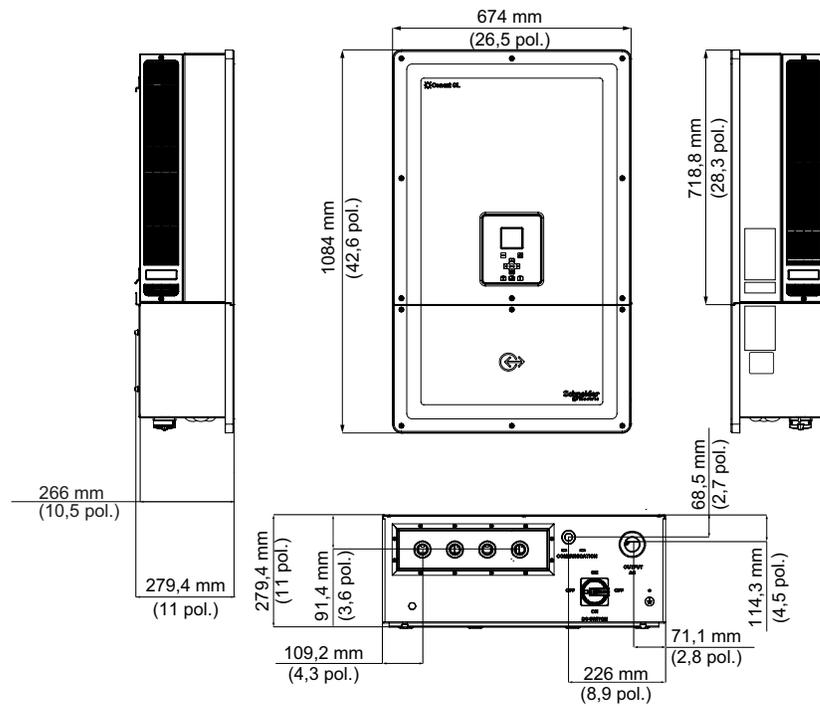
Vistas e dimensões do inversor e da caixa de ligações (Essential/Optimum)
